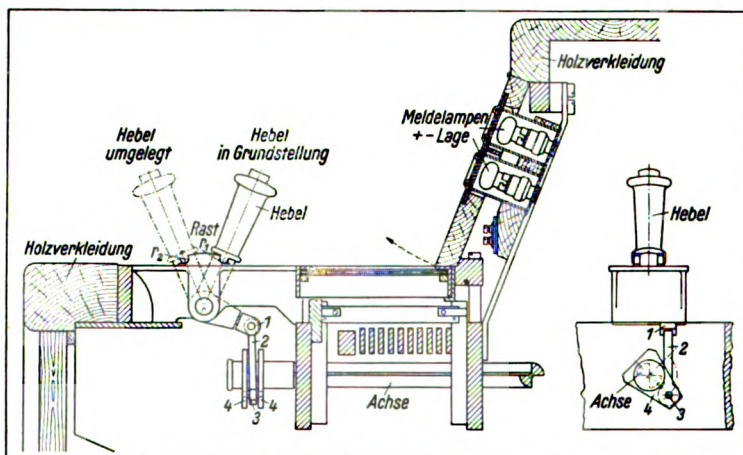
Querschnitt des Siemens-Schalterwerkes.
